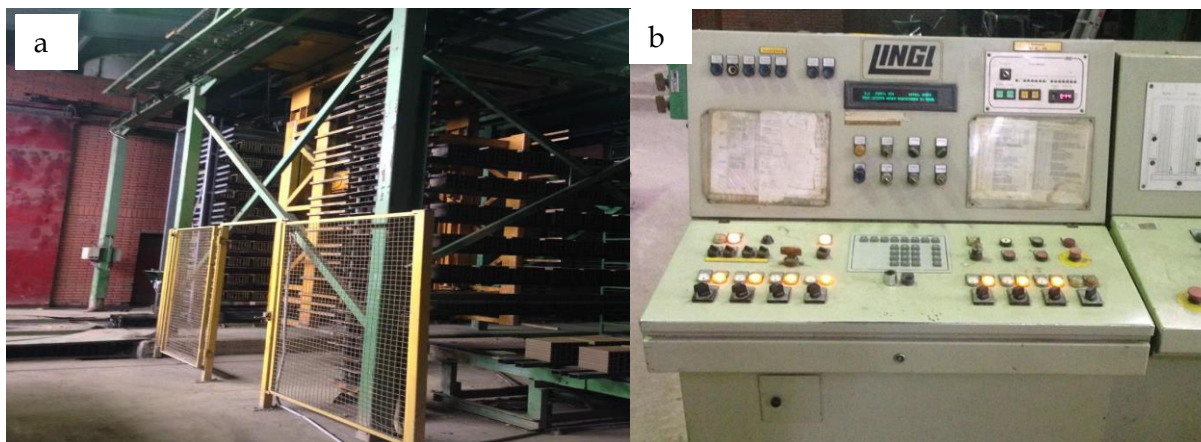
a) elevatori –pjesa e jashtme dhe b) pulti komandues i rrotullueses, elevatorit dhe laderenit.
